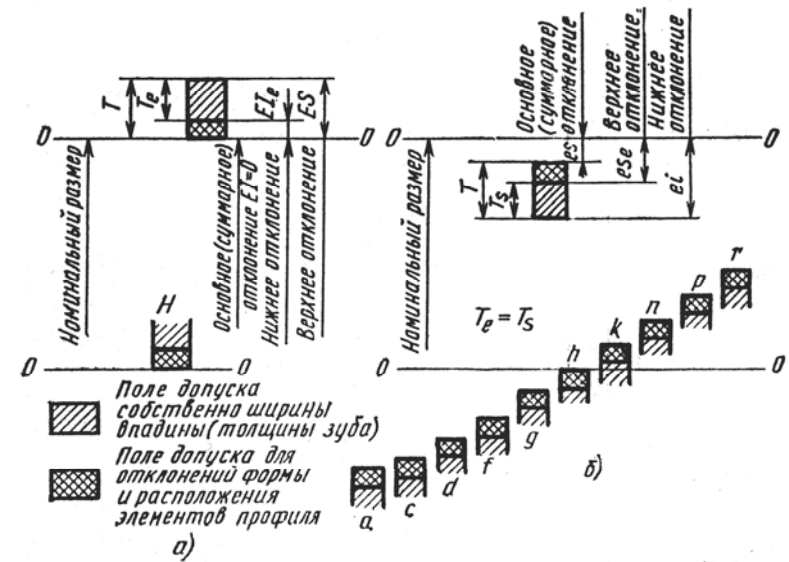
Расположение полей допусков ширины e впадины втулки (а) и толщины s зуба вала (б) в эвольвентных соединениях
